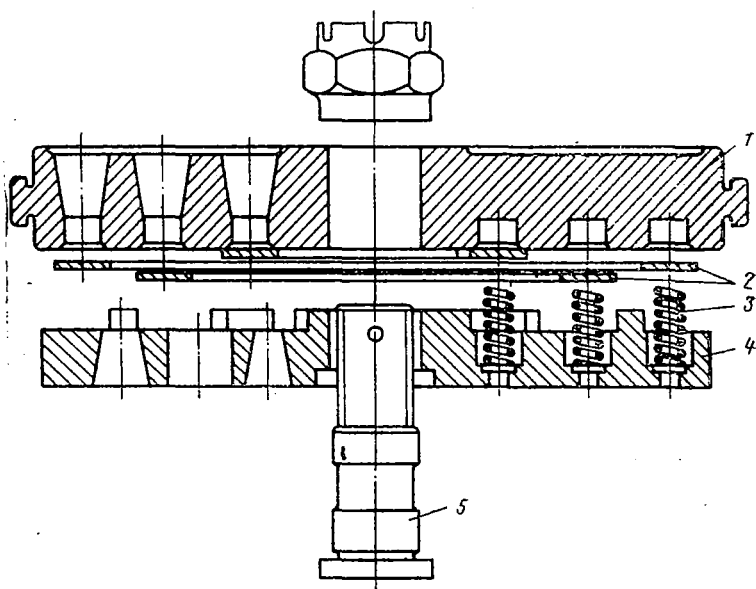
Пластинчатый кольцевой клапан компрессора КС-9
